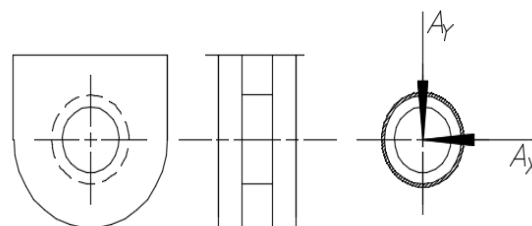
DCL del cordón de soldadura en la unión de las placas del apoyo A
